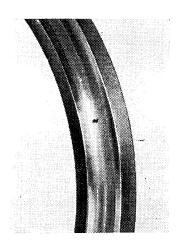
Усталостное выкрашивание на поверхности качения наружного кольца шарикоподшипника
